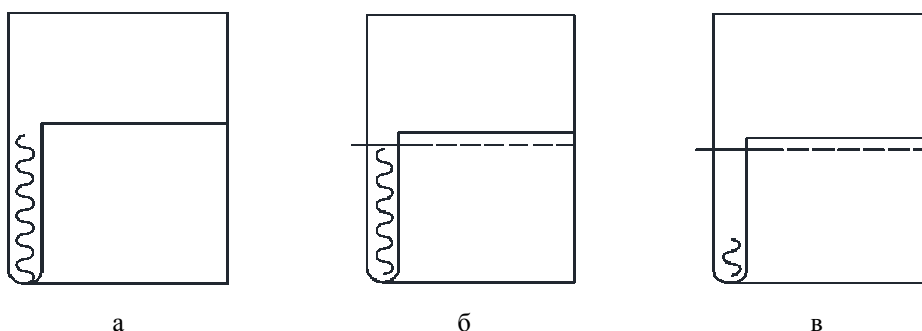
Монтажная схема конструкции низа рукава швом вподгибку с открытым срезом: а – без отделочной строчки; б, в – с отделочной строчкой
